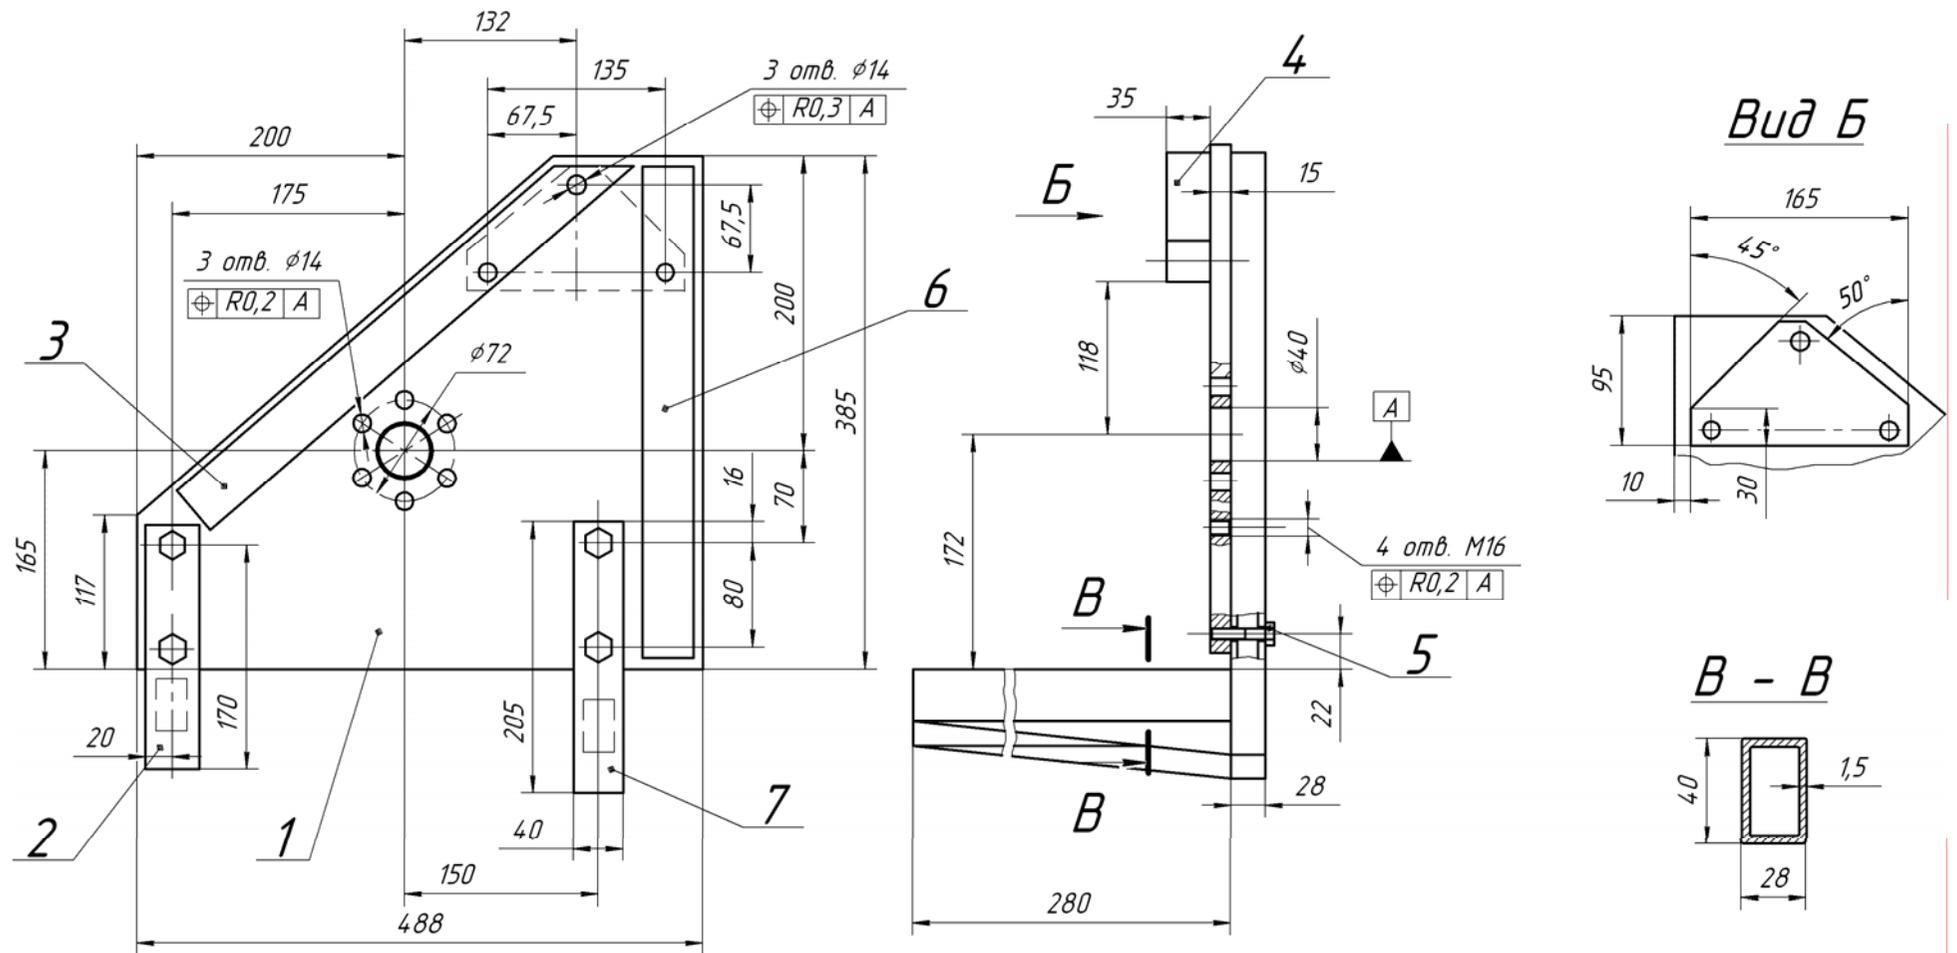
Стенд для сборки и разборки коробки передач КП ЯМЗ-239
